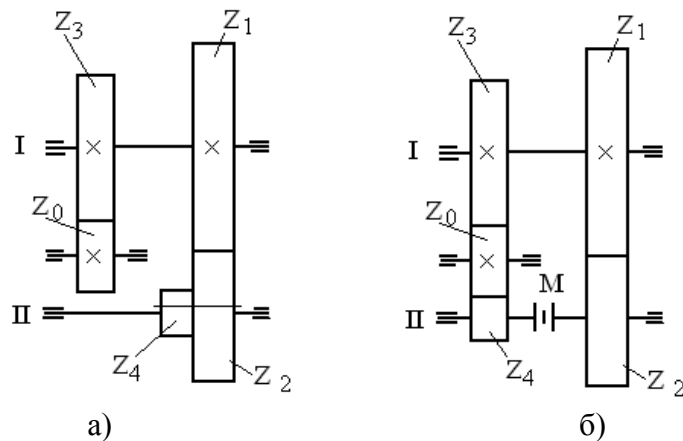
Реверсивные механизмы с цилиндрическими колесами
